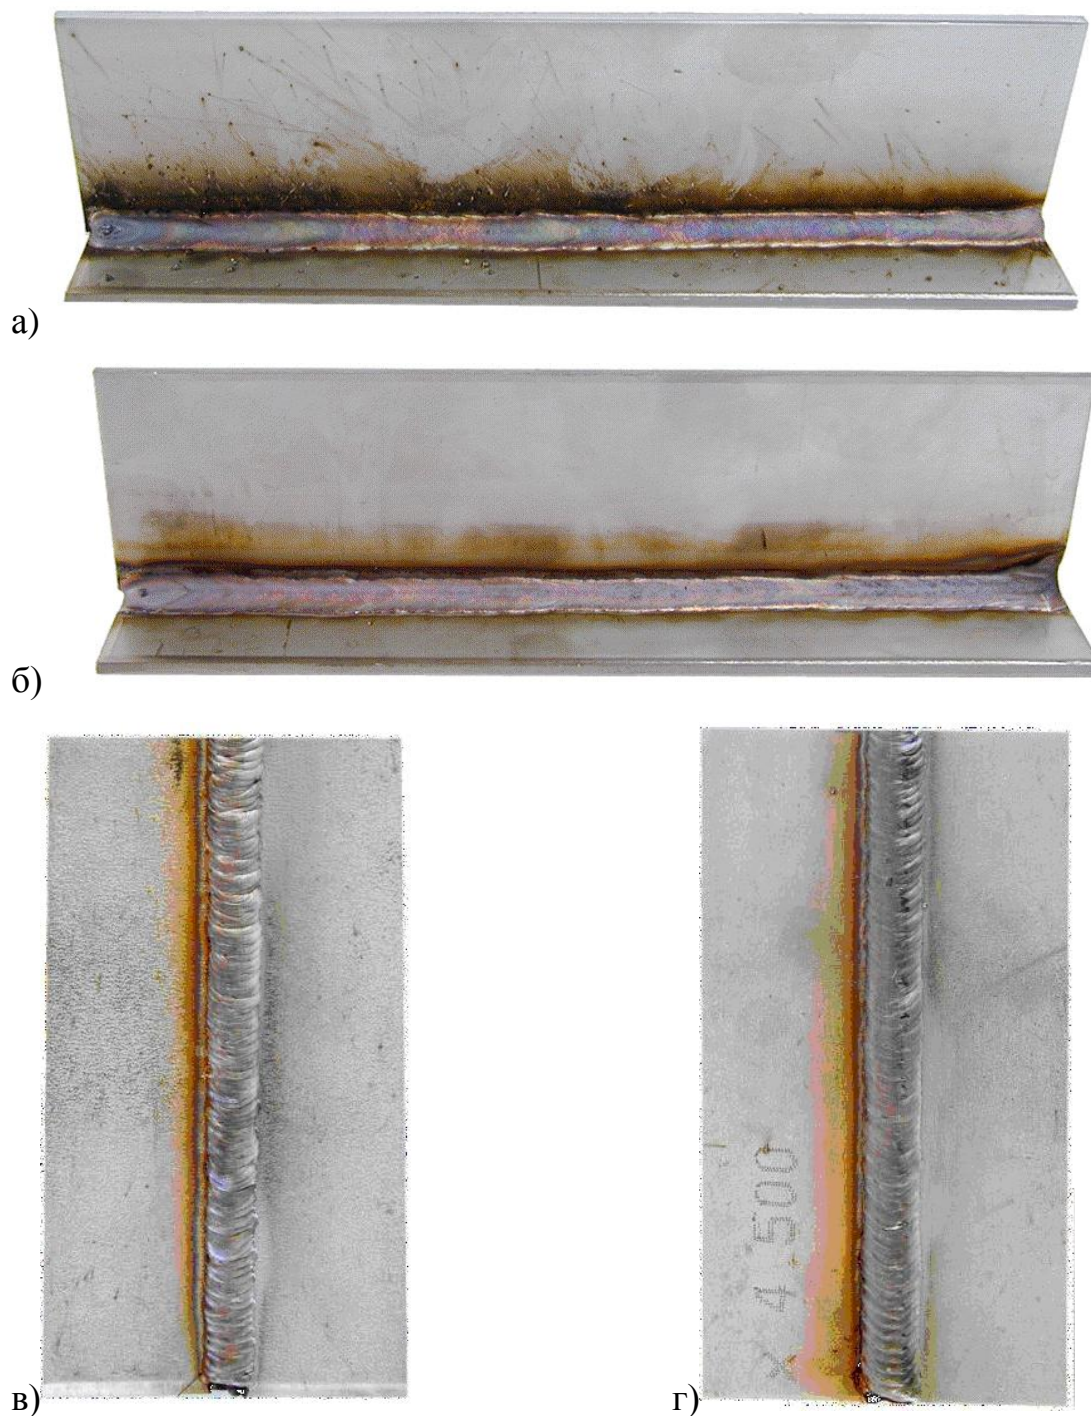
Внешний вид швов, сваренных проволокой  $\varnothing 1$  мм классической MIG сваркой (а, в) и импульсной дугой (б, г): а) тавровое соединение, толщина 4 мм, скорость сварки 0,3 м/мин; б) то же, скорость сварки 60 м/мин; в), г) вертикальный шов, V-разделка, толщина 10 мм
